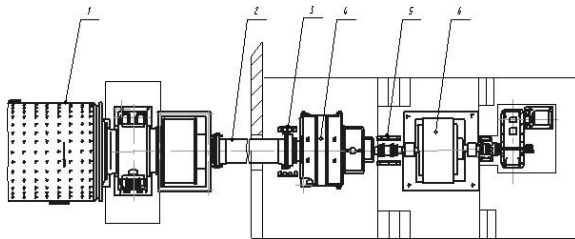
Схема мельницы МЦ-4×13,5: 1-барабан мельницы; 2-промвал; 3-зубчатая муфта тихоходной ступени редуктора; 4-планетарный двухступенчатый редуктор; 5- муфта быстроходной ступени редуктора; 6-синхронный электродвигатель главного привода
